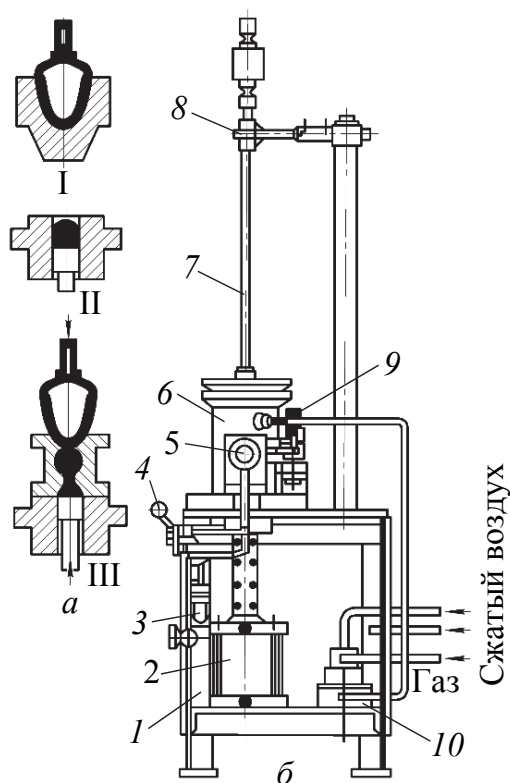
Схема процесса изготовления изделий на ножке способом подпрессовки (а) и общий вид установки (б):
